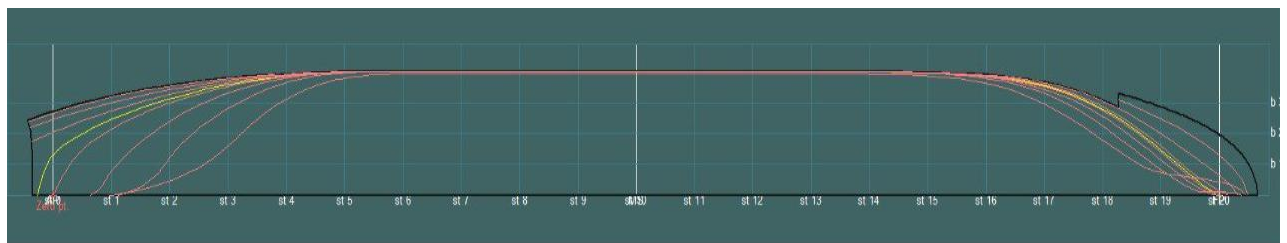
Створена 3D модель теоретичної поверхні корпусу балкера
